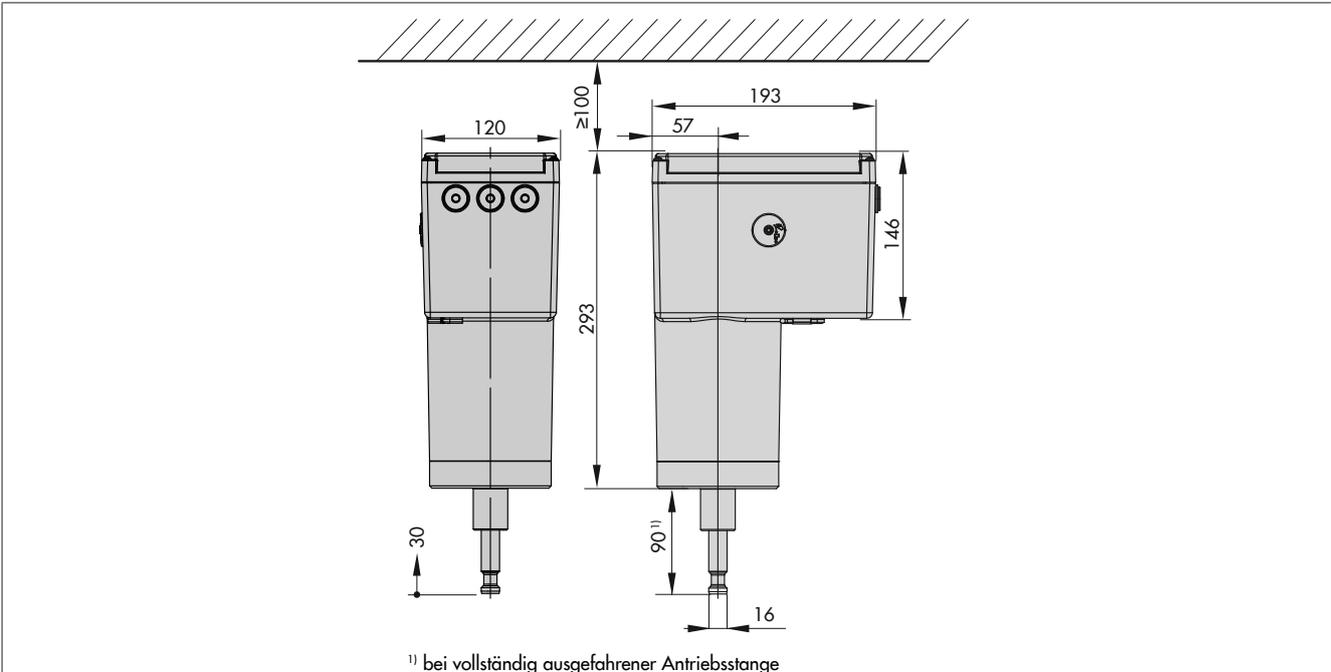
Maße in mm · Typ 3374-25 und -27, Ausführung Form A
